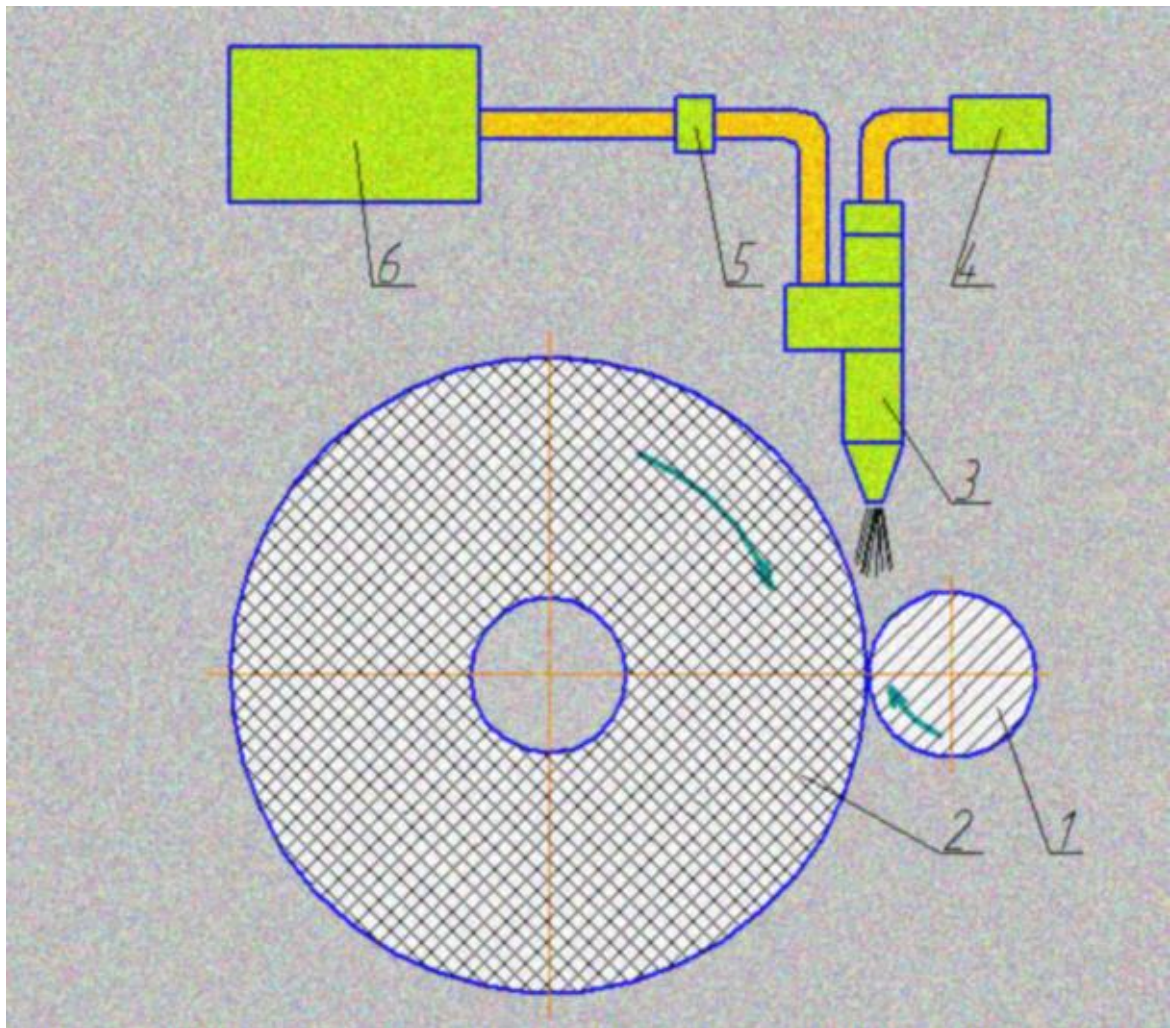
Схема подачи ионизированной газовой среды в зону резания: 1 – заготовка; 2 – шлифовальный круг; 3 – плазмотрон-сопло; 4 – система питания плазмотрона; 5 – регулятор давления газовой среды; 6 – компрессор
